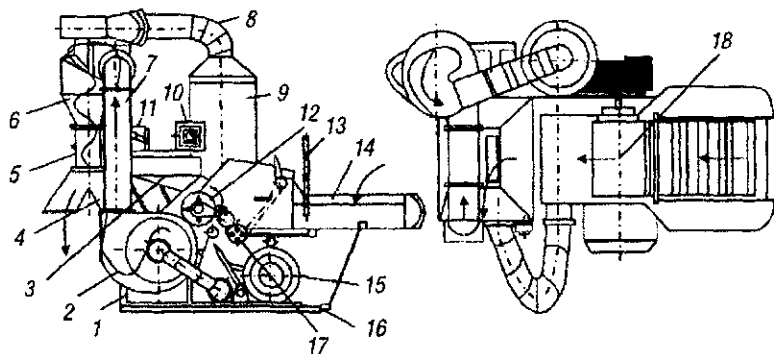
Схема универсальной дробилки кормов КДУ-2,0: 1 – дробильный аппарат; 2 – вентилятор; 3 – загрузочный бункер; 4 – рукав выгрузки; 5 – шлюзовый затвор; 6 – циклон; 7, 8 – кормовой и воздушный трубопроводы; 9 – фильтрованный рукав; 10 – амперметр-индикатор; 11 – червячный редуктор; 12 – ножевой барабан; 13 – рычаг включения; 14, 18 – подающий и прессующий транспортеры; 15 – электродвигатель; 16 – рама; 17 – редуктор
